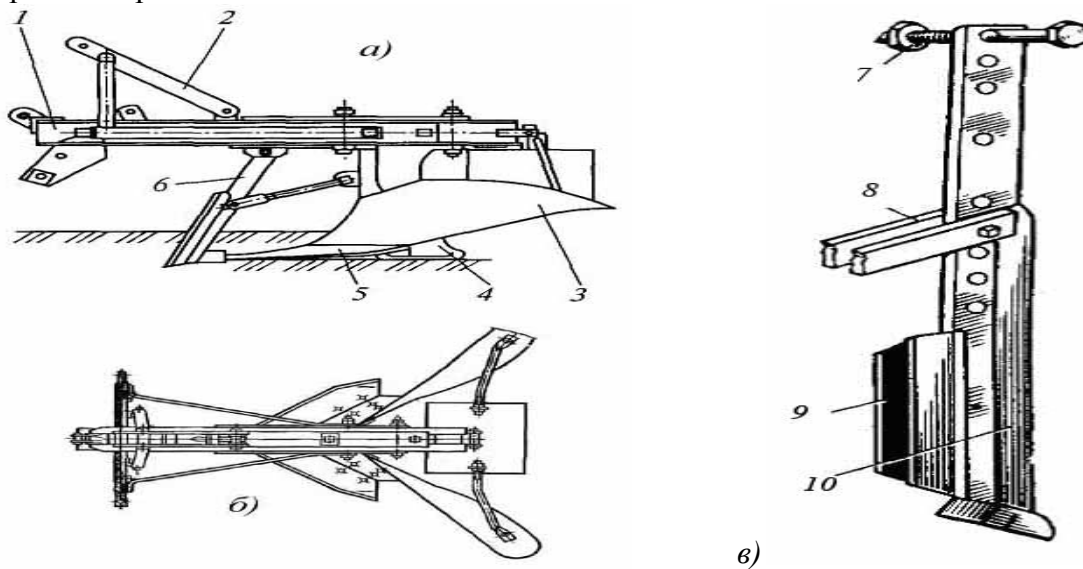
Плуг ПКЛ-70 (двухотвальнй корпус) с установленным черенковым ножом: а) вид сбоку: 1 — рама; 2 — навесное устройство; 3 — корпус плуга; 4 — опорная пята; 5 — лемех; 6 — черенковый нож; б) вид сверху; в) черенковый нож с прямым резцом: 7 - болт специальный, 8 — тяга, 9 — направляющая резца, 10 — резец с долотом
